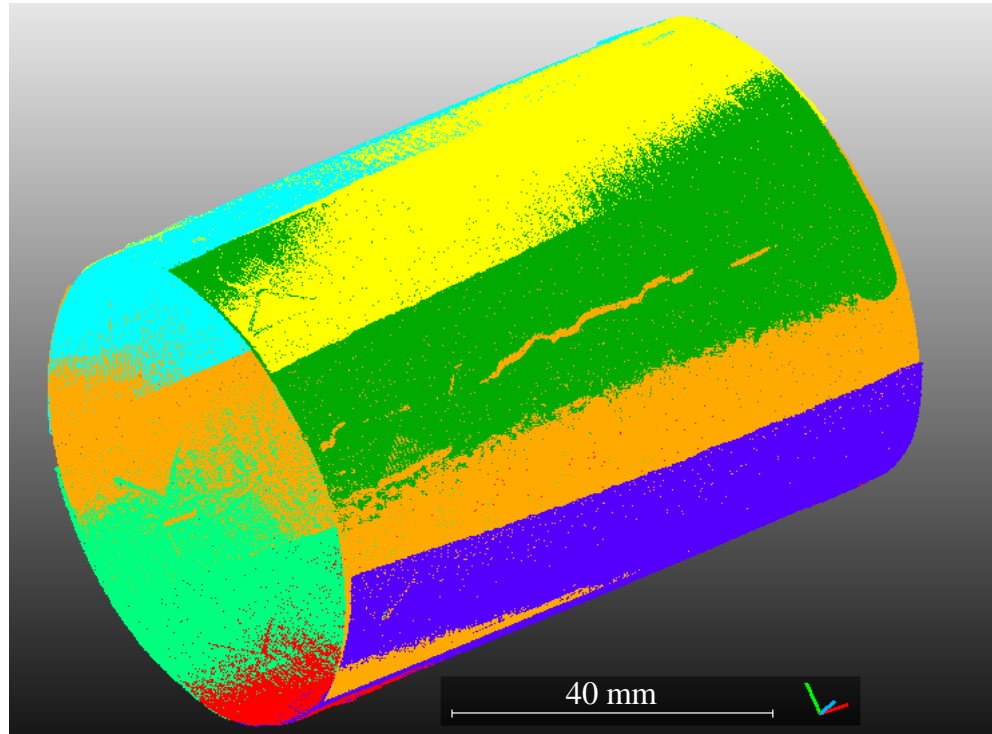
Reconstrucción 3D de la tubería a 360° de observación.
